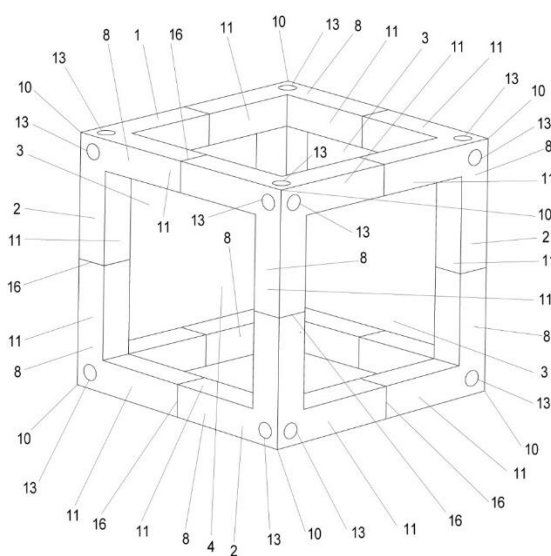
Рама приспособления – спутника в сборе, аксонометрия.
